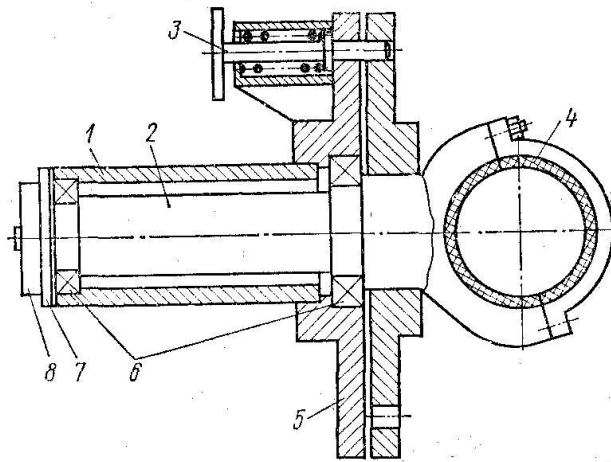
Схема пристрою для збирання колінчастих валів:
